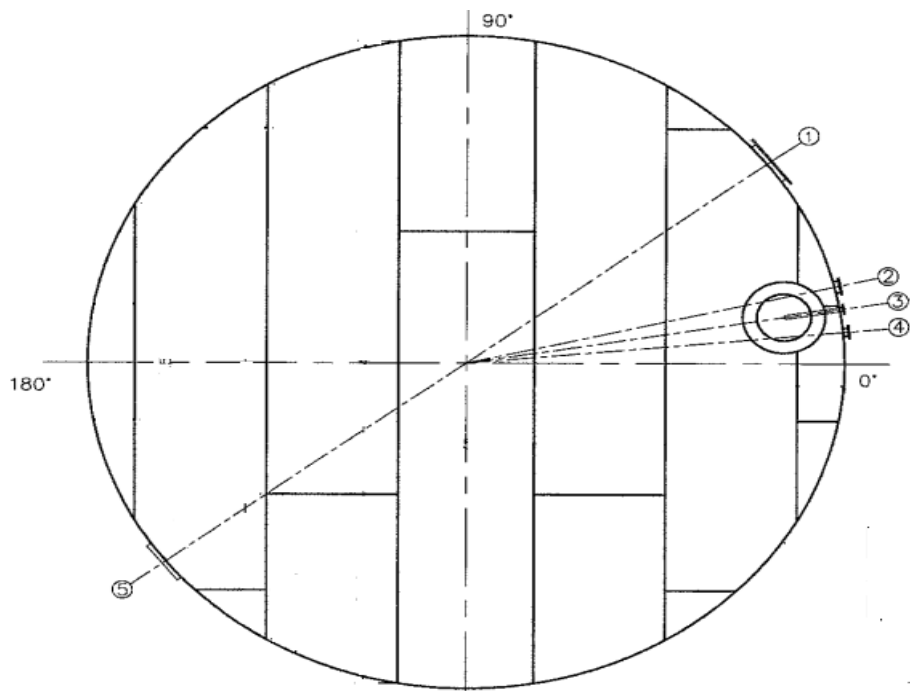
Vista superior de los accesorios del tanque de techo fijo
